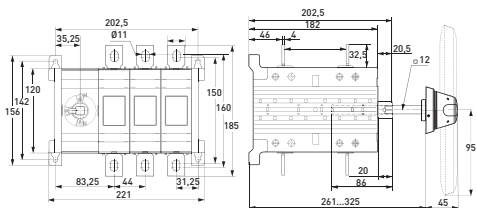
Габаритные и установочные размеры реверсивных рубильников 315-400А 3Р
